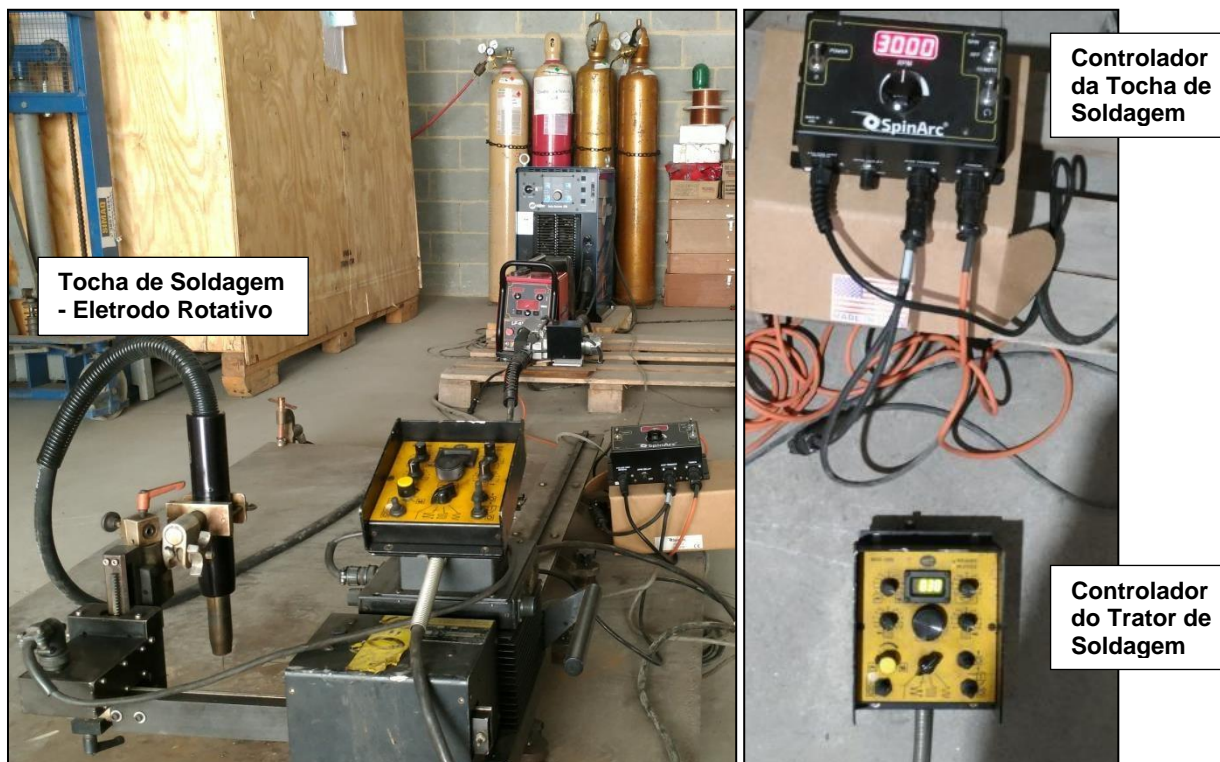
Montagem dos equipamentos para soldagem [12].
